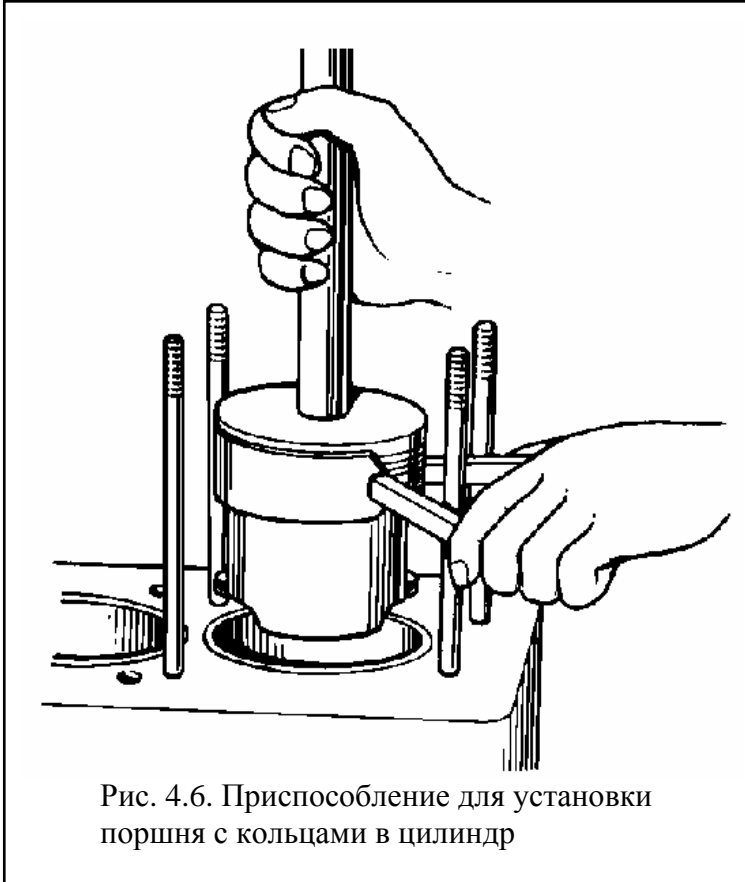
Приспособление для установки поршня с кольцами в цилиндр
